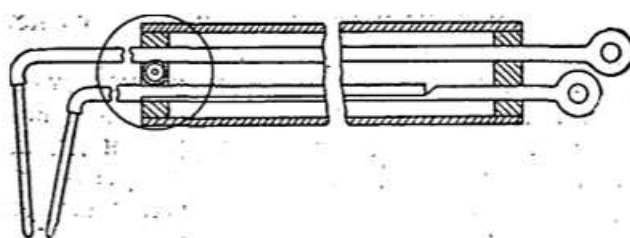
Схема примитивного держателя для сварки раздельными электродами.
